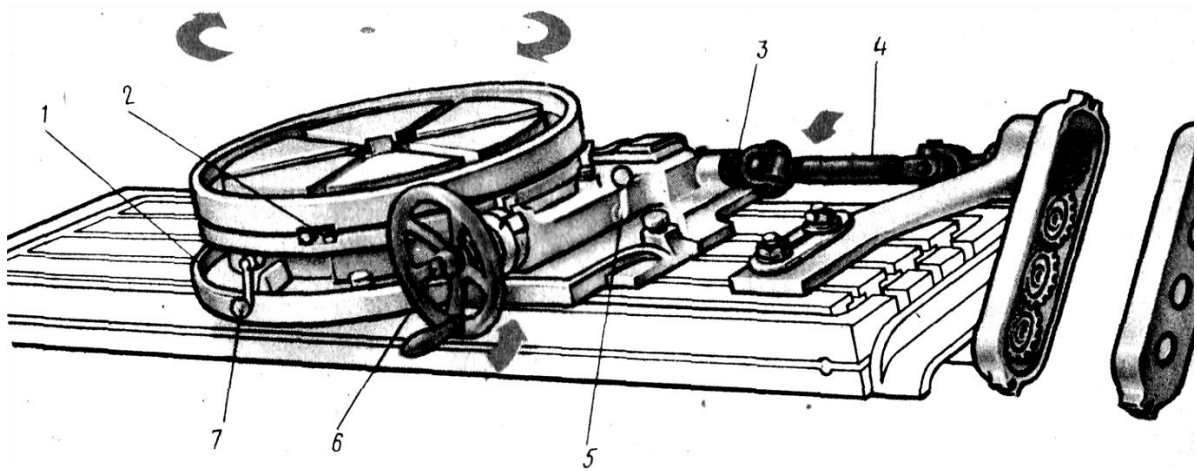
Круглий поворотний стіл з ручним механічним приводом
